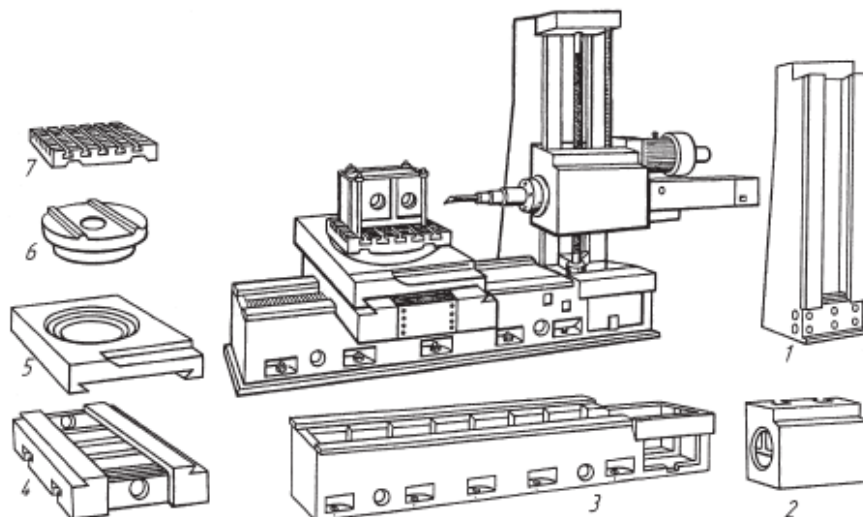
Базові деталі фрезерно-розточувального верстата. 1 – стійка; 2 – шпиндельна бабка; 3 – станина; 4 – нижні салазки; 5 – верхні салазки; 6 – поворотний стіл; 7 – монтажна плита.
